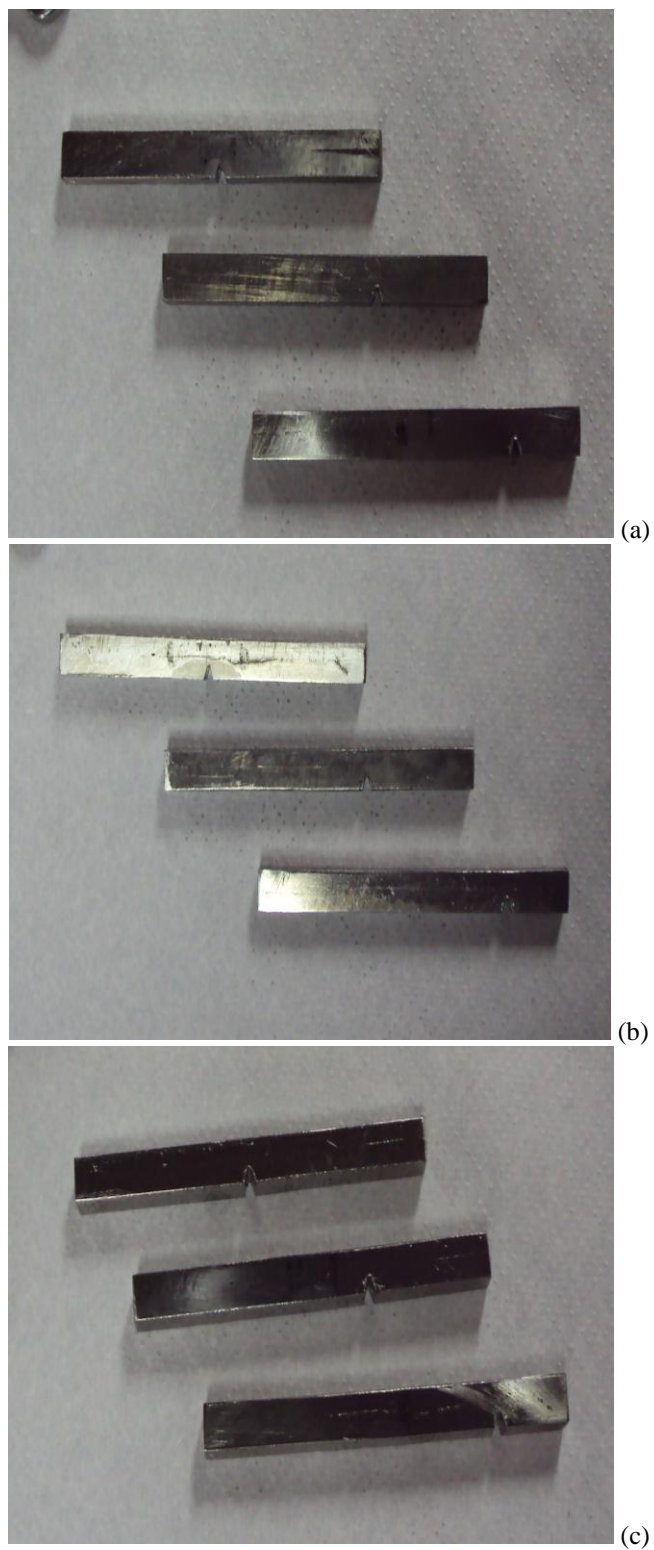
Imagens dos corpos de prova para o ensaio de impacto – (a) CPs soldados com parâmetro de soldagem 1 e entalhes no cordão, na ZTA e no metal de base; (b) CPs soldados com parâmetro de soldagem 2 e
